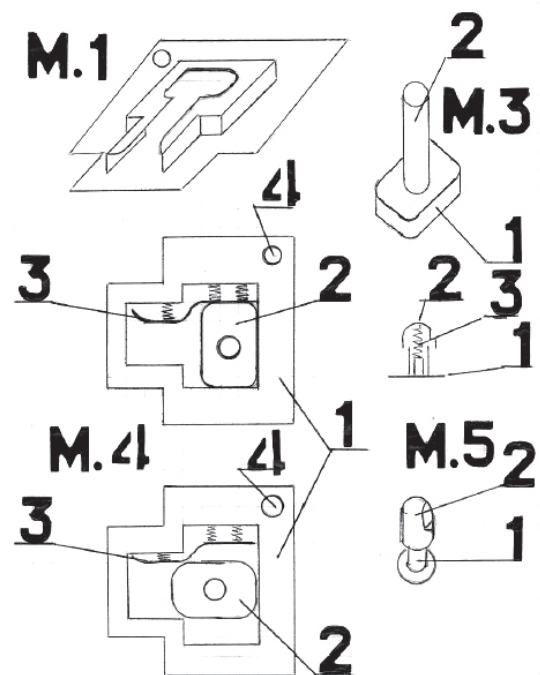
(М.4) - схема спрацювання у корпусі замка пластини с пружинами та стрижня с кулачком. В одному варіанті кулачок фіксується в корпусі пластиною с пружинами, а при повороті кулачка фіксація відсутня. 1 - пластина на якій кріпиться корпус замка (М.1), 2 - кулачок із стрижнем (М.3), 3 - пластина з пружинами (М.2), 4 - отвір під додатковий запобіжник - кнопки з головкою на пружині (М.5).
